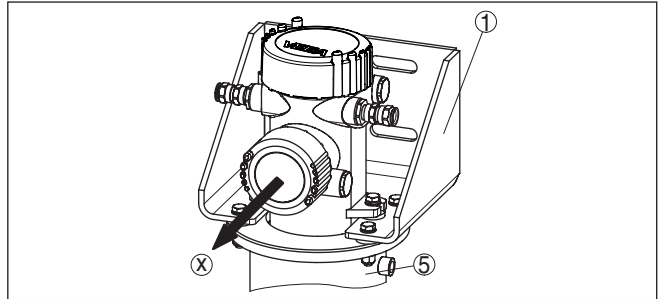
Montagerichting van de sensor ten opzichte van de bevestigingsbeugel
